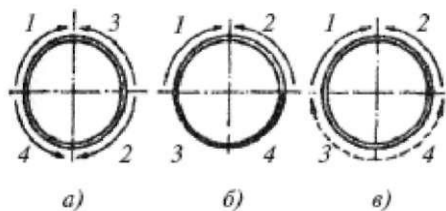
Последовательность сварки труб большого диаметра: а - (200—300) мм; б - (500—600) мм; в - сварка без поворота трубы
